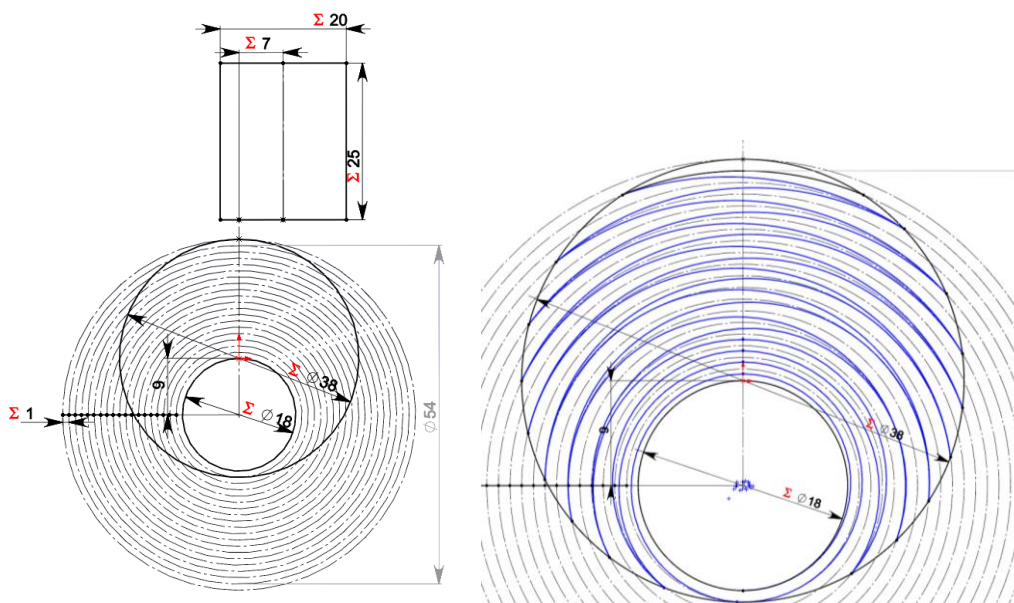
Траектория движения фрезы при черновой обработке.
